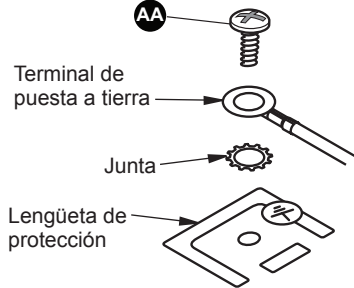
Instalación de terminal de puesta a tierra a la cubierta superior
